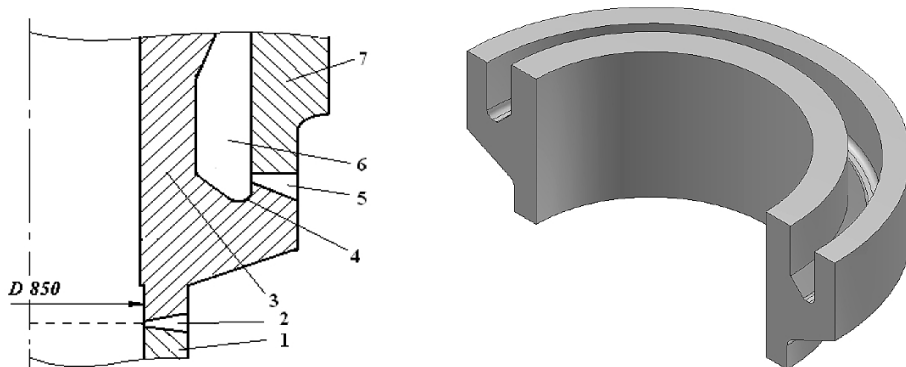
Фрагмент конструкции узла соединения горячего коллектора с корпусом ПГ: 1 – ГЦТ; 2 – сварной шов; 3 – коллектор ПГ; 4 – галтель; 5 – СШ № 111; 6 – карман; 7 – патрубок ПГ.
